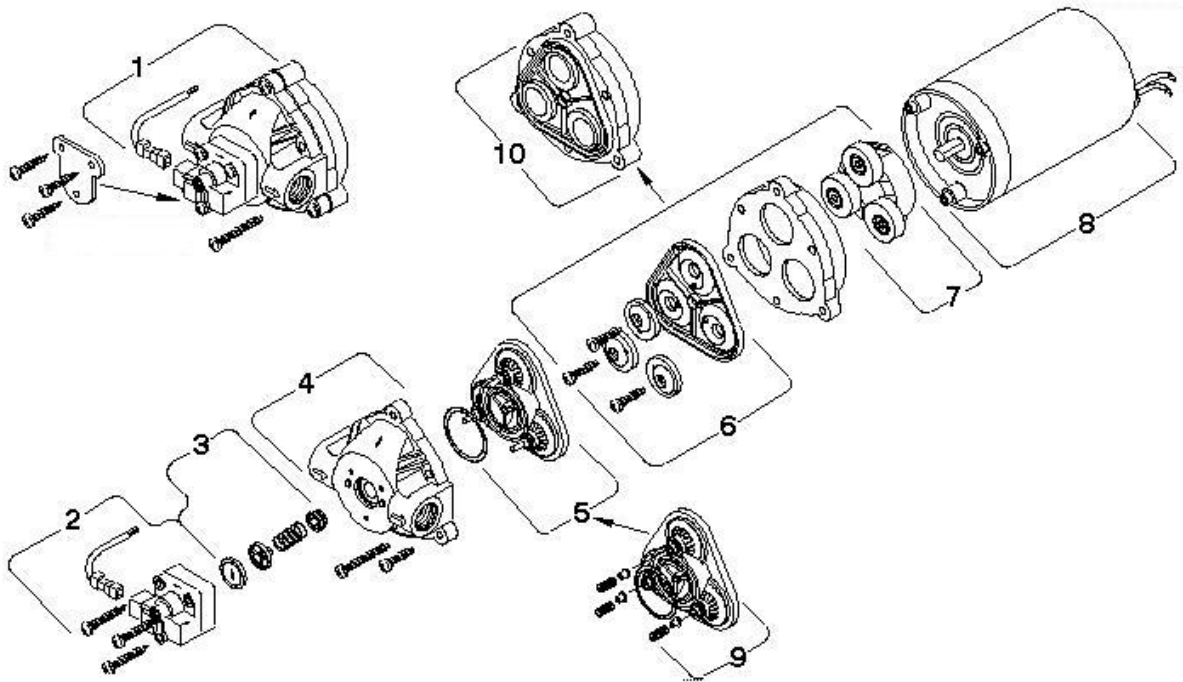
Vista explodida do conjunto motor e bomba de diafragma Shurflo modelo 8000 – 443 – 136. O desenho foi fornecido pelo fabricante.
